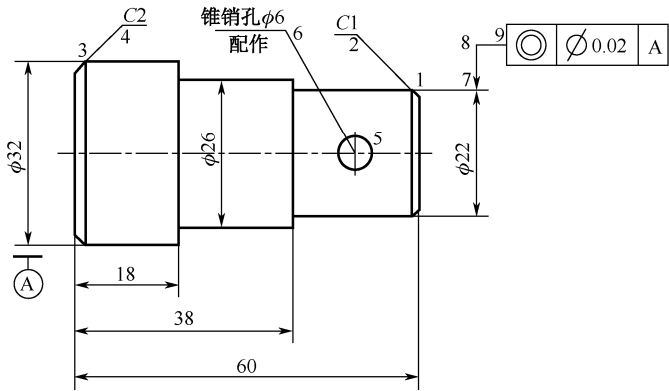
标注倒角、销孔尺寸及形位公差
